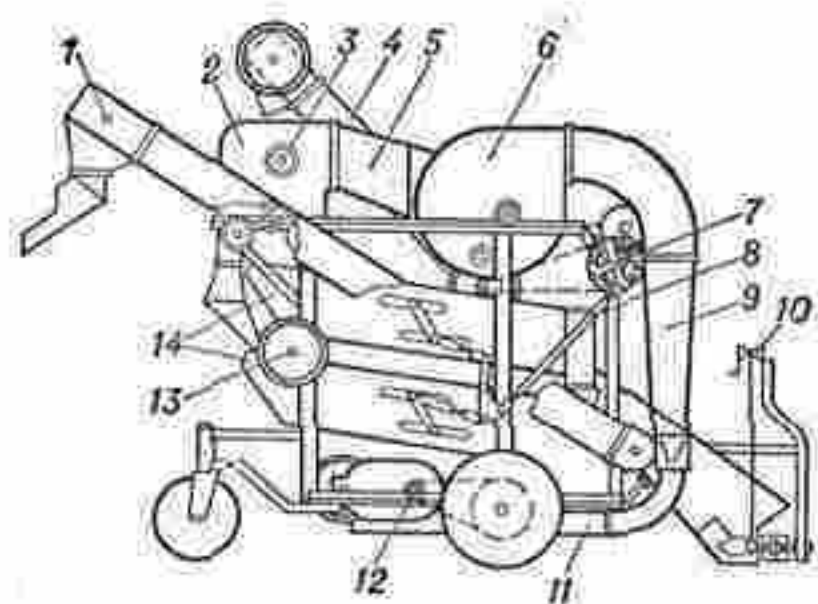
Зерноочистительная машина ОВП-20: 1 — отгрузочный транспортер; 2 — приёмная камера; 3 — шнек; 4 — загрузочный транспортер; 5 — воздуховод; 6 — вентилятор; 7 — приводной вал; 8 — шатун; 9 — инерционный пылеотделитель; 10 — лебедка подъёма питателя; 11 — пневмотранспортер отходов; 12 — механизм самопередвижения; 13 — эксцентриковый вал; 14 — решётный стан.
